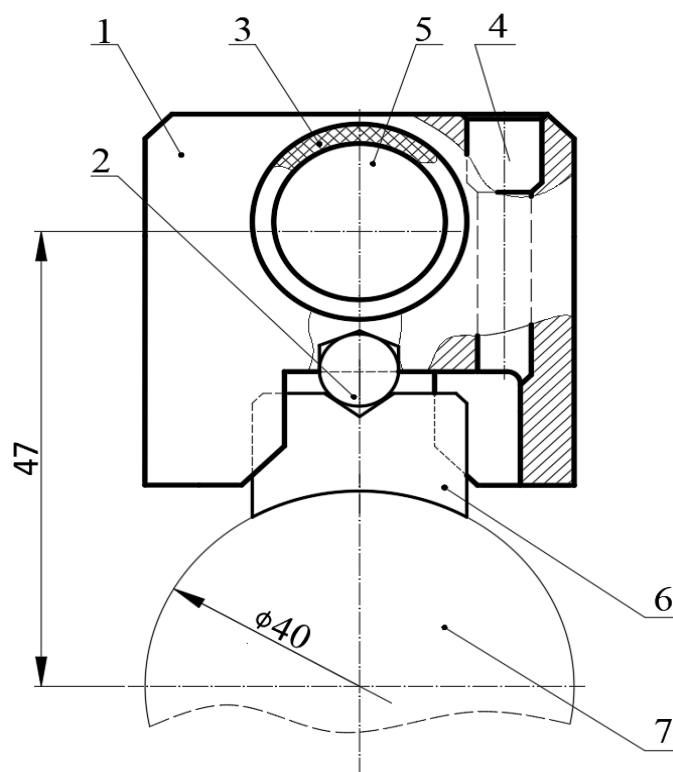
Схема базирования и установки колодки [5М]:
